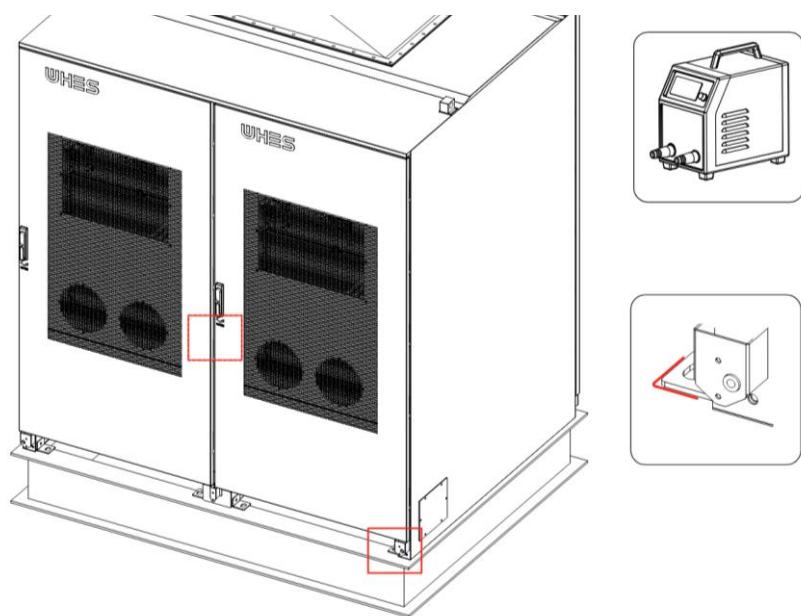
Es wird am Metallsockel schweißt
